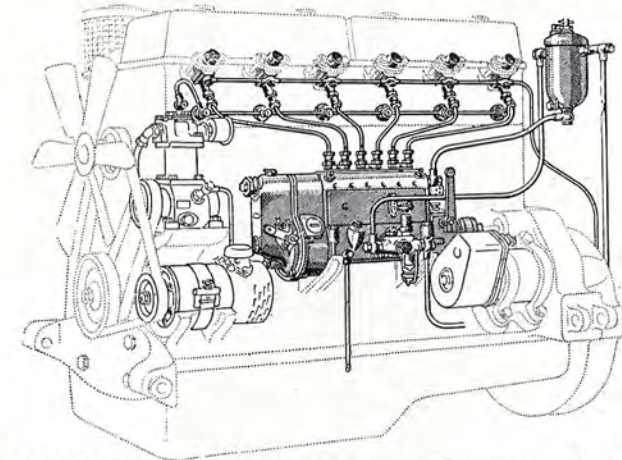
BOSCH-Ausrüstung für Diesel-Motoren mit Einspritzpumpe PE 6 B
